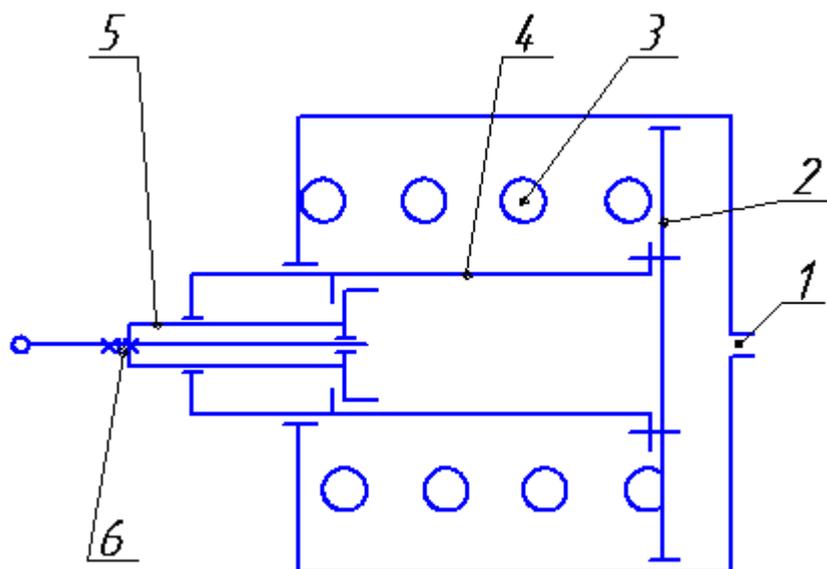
Схема пневматичного пружинного енергоакумулятора
